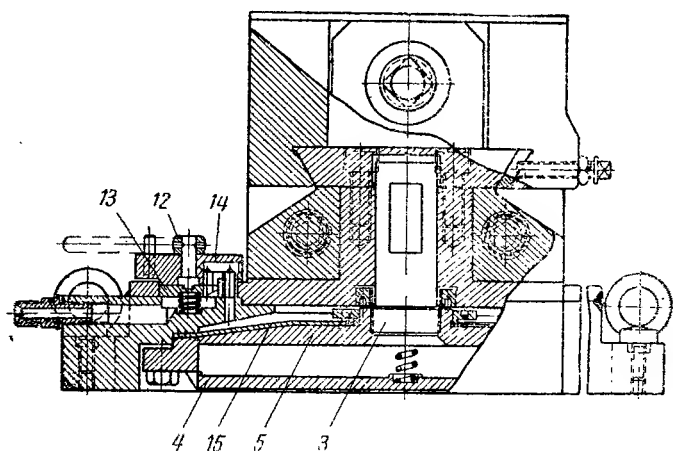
Пневматические тиски для крепления коллекторных пластин при фрезеровании шлица
